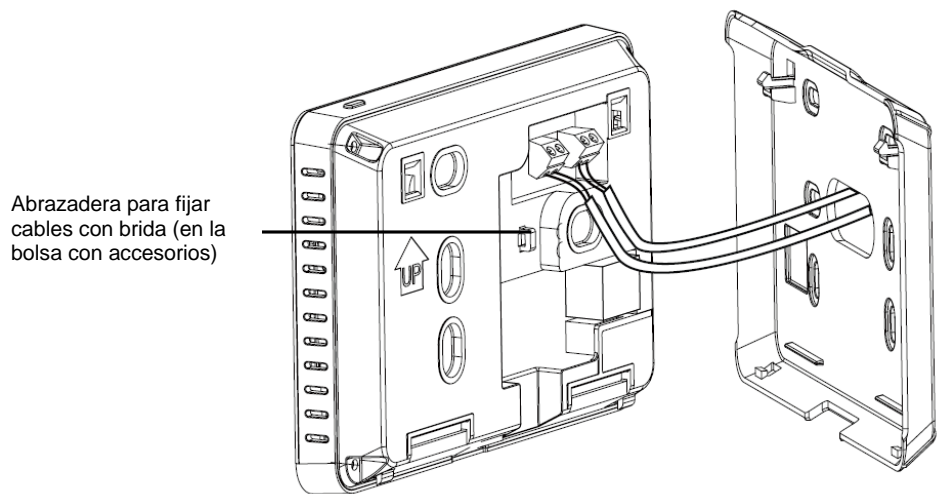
Conexión de los cables al mando central y abrazadera para la brida de los cables
